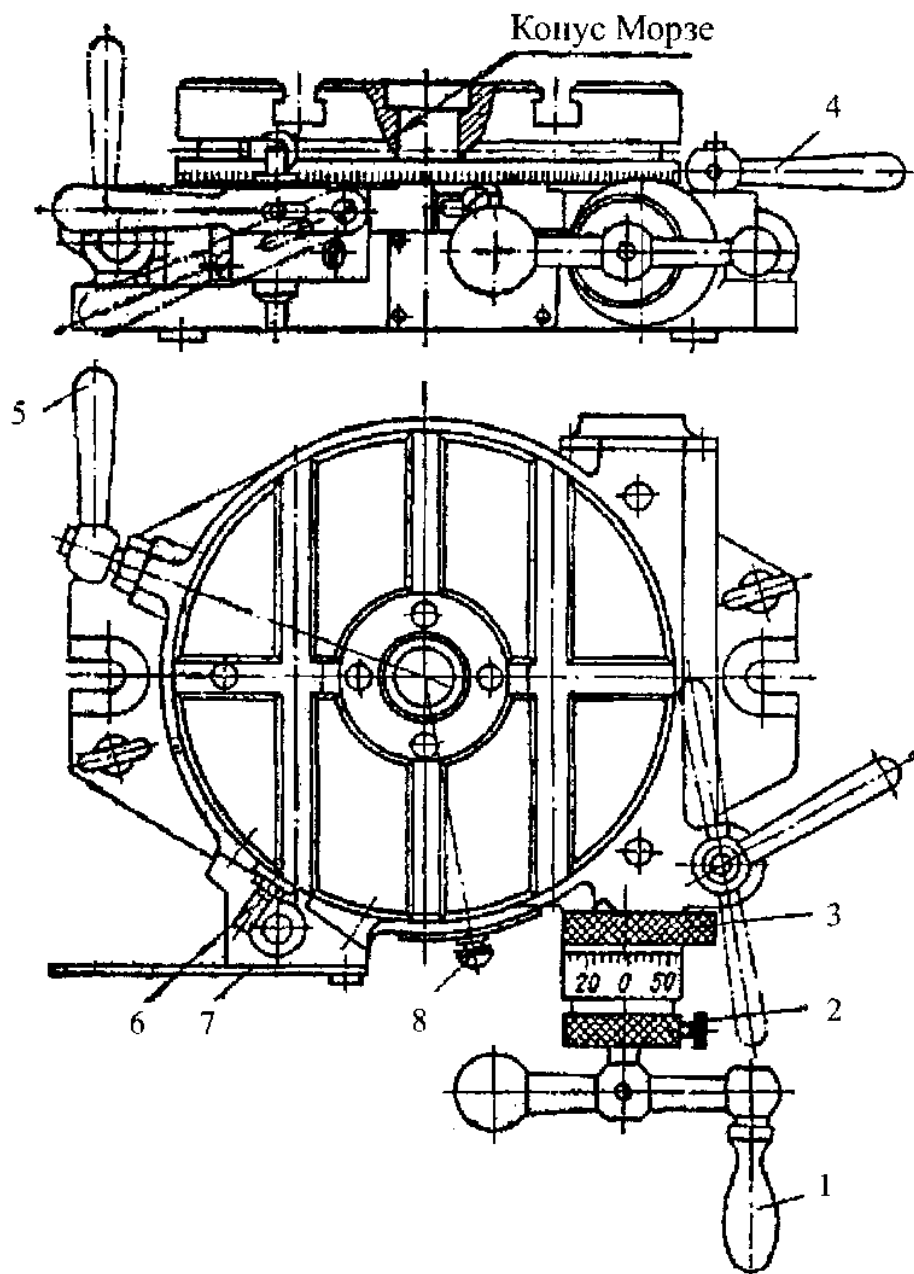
Загальний вид стандартного поворотного стола з ручним приводом
